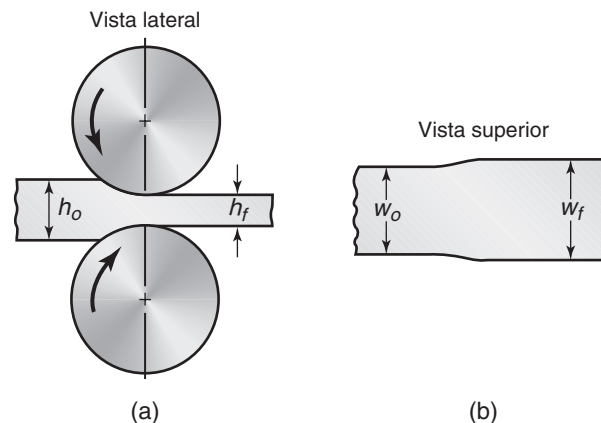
Aumento de la anchura de la cinta (ensanchado) en el laminado plano. Note que se puede observar un ensanchado similar a cuando la masa para pan se lamina con un rodillo.
